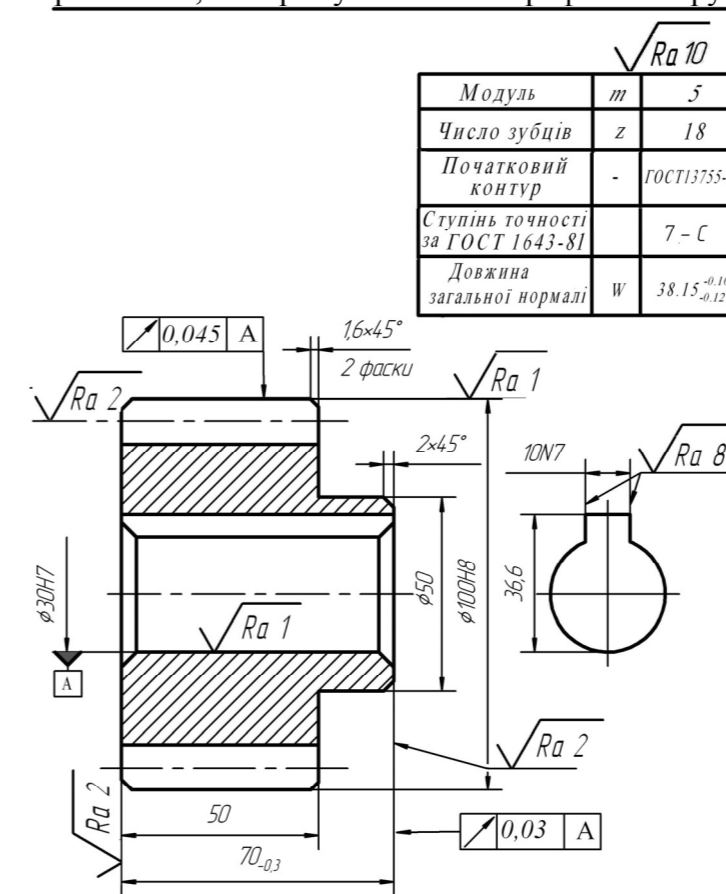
Приклад робочого кресленика циліндричного зубчастого колеса з прямими зубцями
